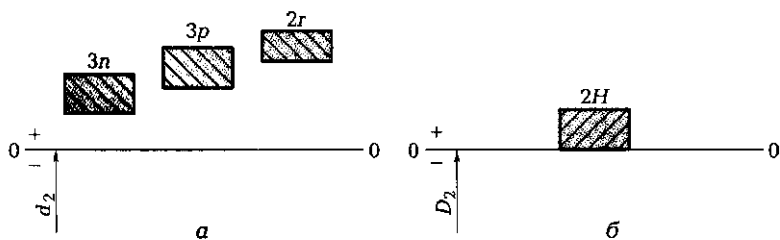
Расположение полей допусков резьбы с натягом:
